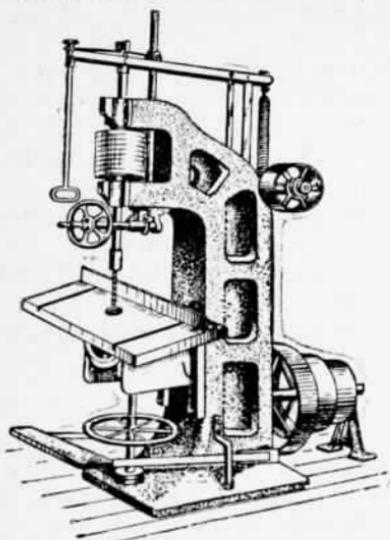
а. Вертикальный сверлильный станок тяжелой модели.
